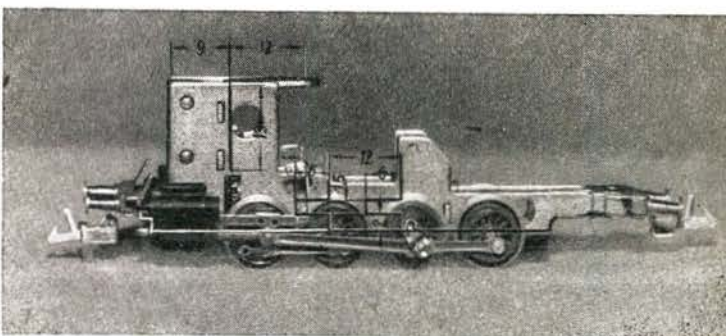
Der Rahmen der BR 81 mit eingezeichneten Änderungen zur BR 80
